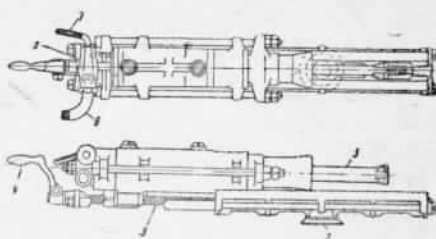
Пневматический молоток для бурения с треноги или колонки: 1 — крышка; 2 — устройство для укрепления на колонке; 3 — винт; 4 — ручка; 5 — бур; 6 — патрубок для воздушного шланга; 7 — патрубок для водяного шланга
